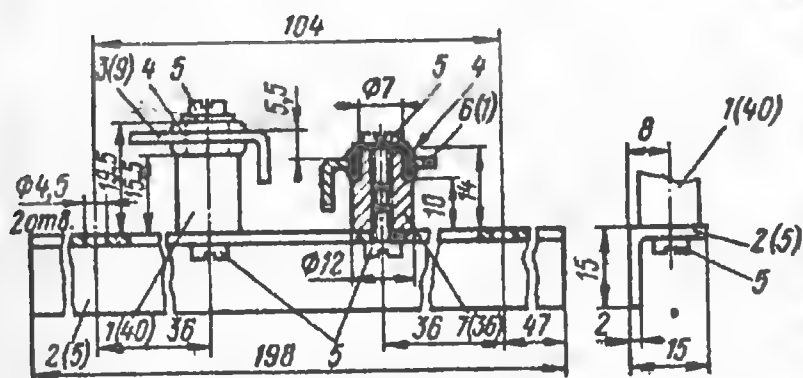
Узел крепления шасси ЛПМ: 1(40), 7(36) — стойки резьбовые, Д16-Т, по 4 шт., закрепить на дет. 2(5) винтами 3; 2(5) — прокладкой, уголок дюралюминиевый [Д16-Т], 2 шт.; 3(9) — шасси блока параметров, закрепить на дет. 1(40) винтами 3, под головку подложить стальные шайбы 3; 4 — опора, резина, 8 шт., вставить в отверстия диаметром 10 мм в дет. 3(9) и 6(1); 5 — винт М4Х6, 8 шт.; 6(1) — шасси узла поддующего вала, закрепить на дет. 7(36) винтами 3
